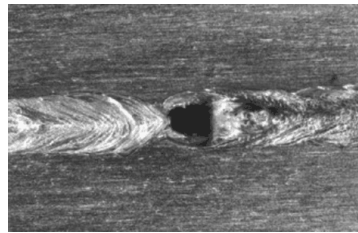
Typischer Auswurf einer Schweißnaht in Aluminium [11].
